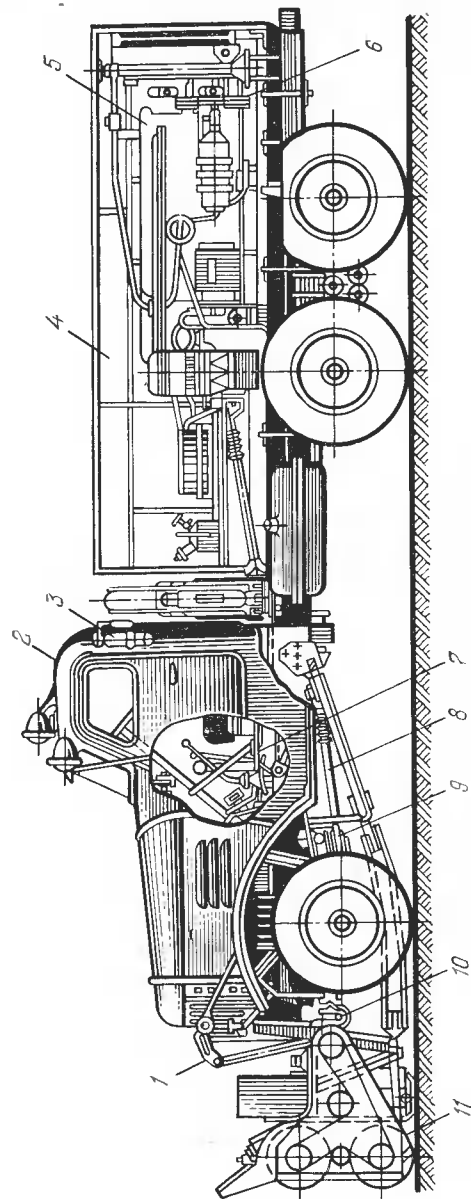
Шнекороторный снегоочиститель ДЭ-204
